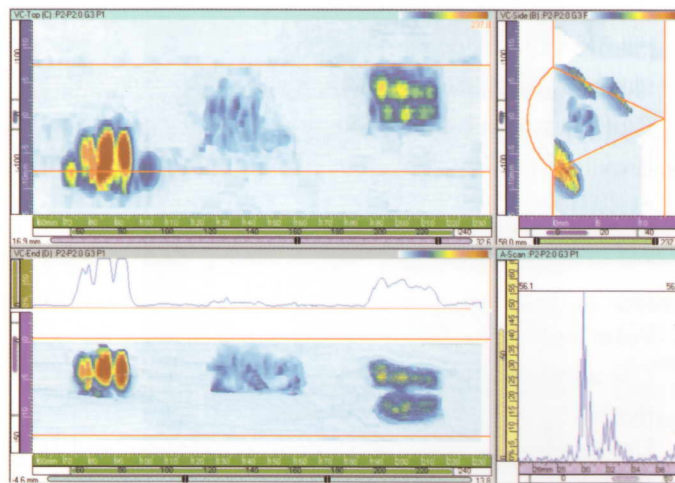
Типичные виды сварного шва, отображающие расположение и форму дефектов
